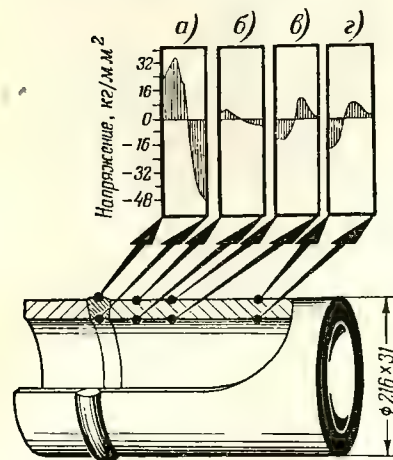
Распределение тангенциальных напряжений вблизи сварного стыка у трубы, изготовленной из аустенитной стали марки 1Х18Н12Т.
